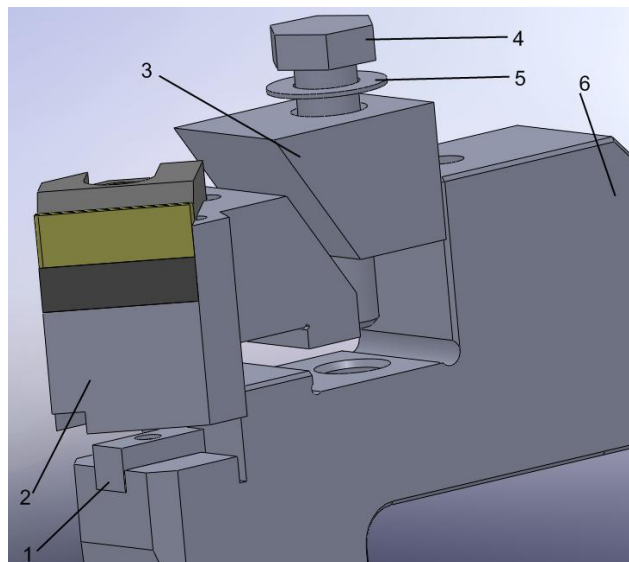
Общий вид рассматриваемого модульного инструмента
